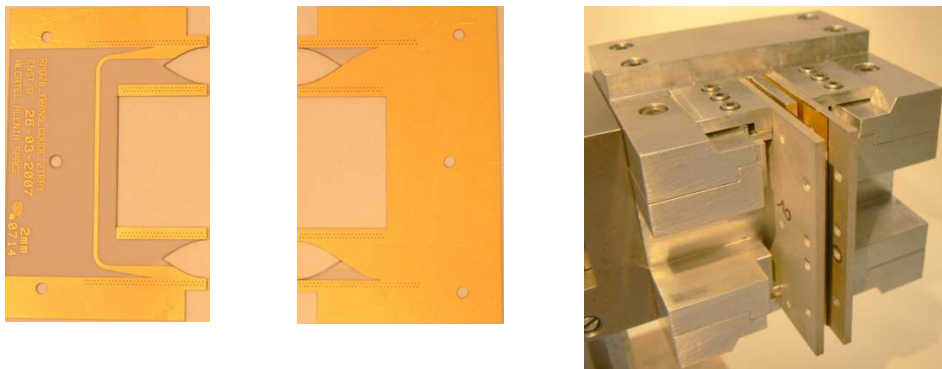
Vue en coupe du diviseur/combinez 16 voies
